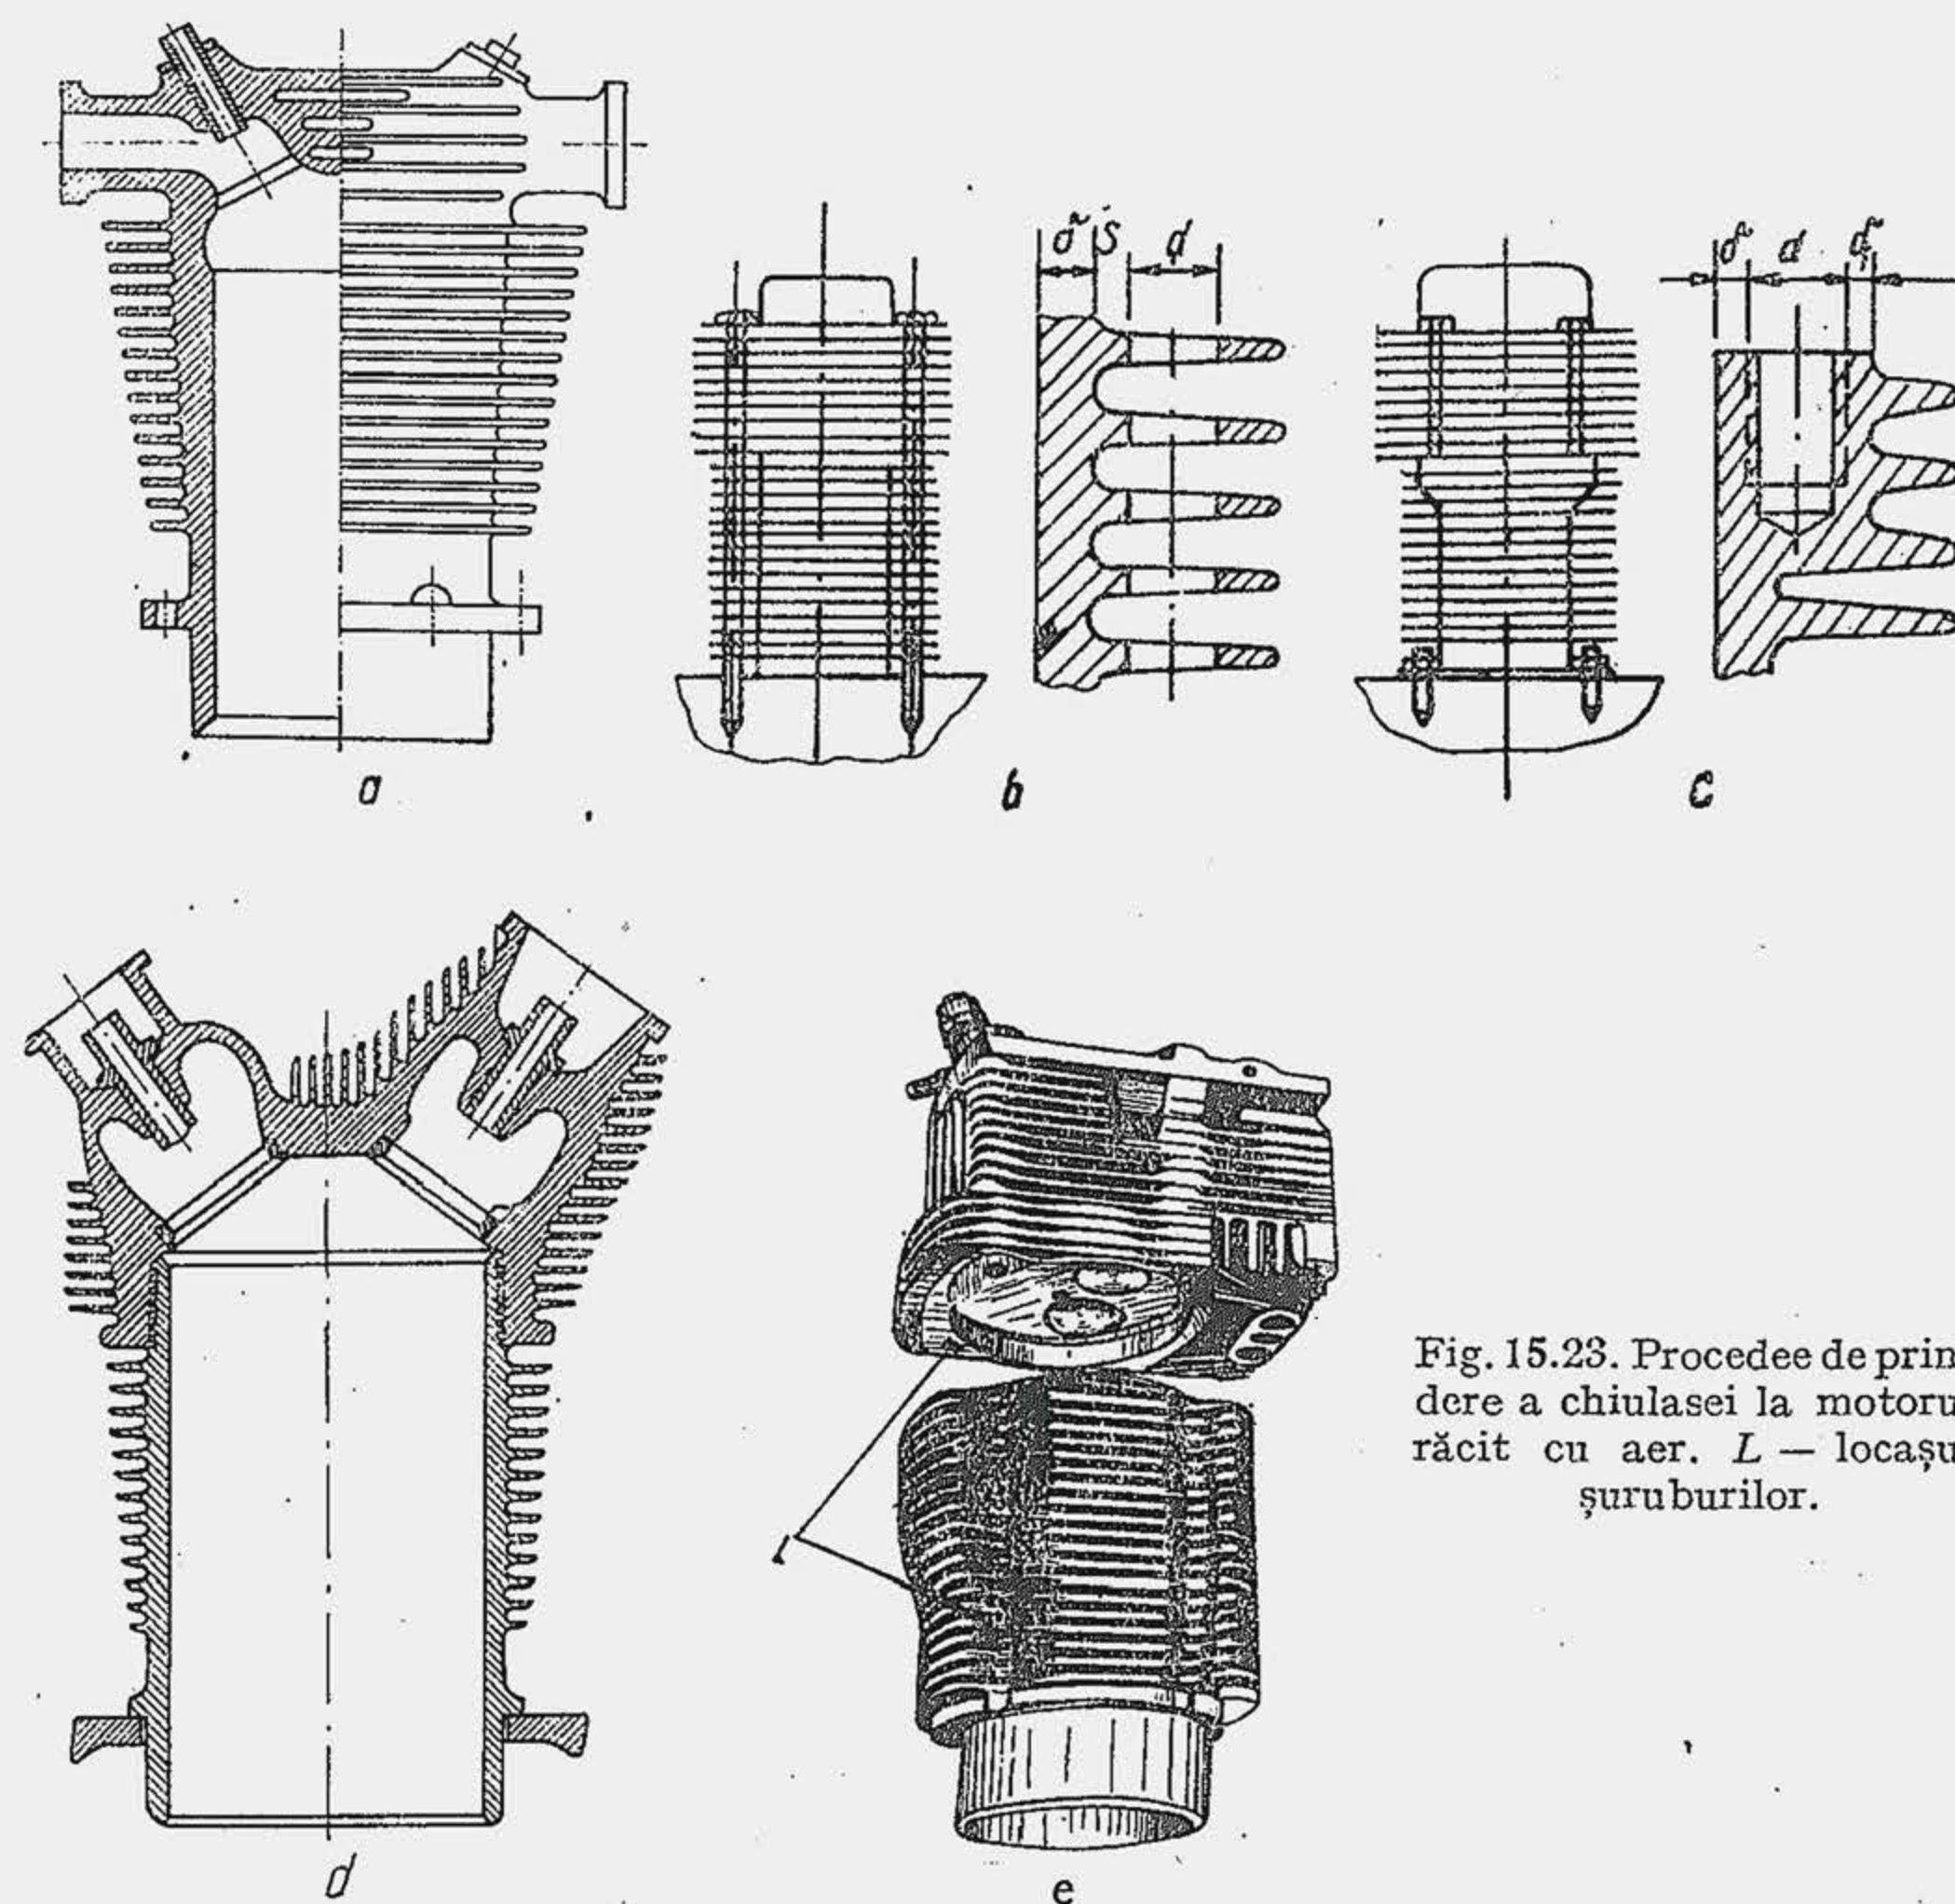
Procedee de prindere a chiulasei la motorul răcit cu aer. L — locașul șuruburilor.
